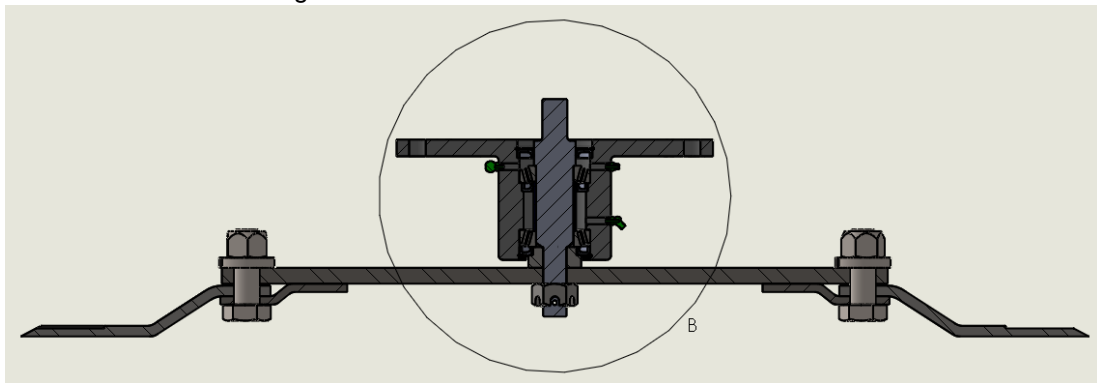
Vista en corte del ensamble inferior del rotor de corte.
